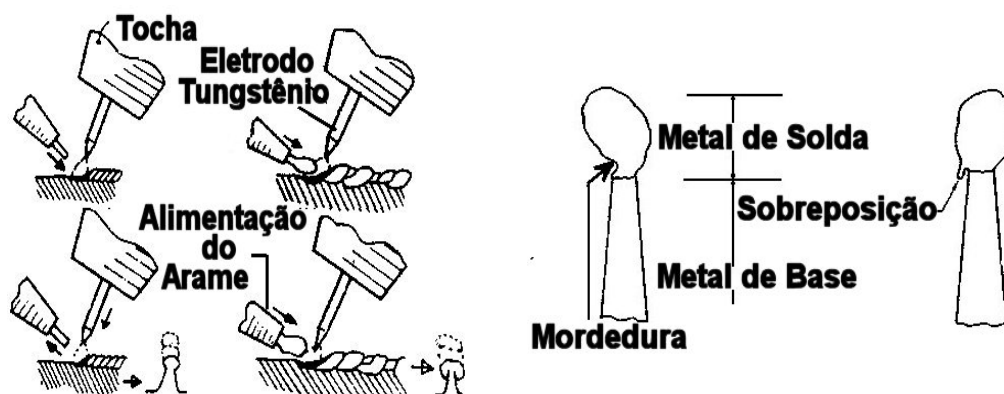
Soldagem TIG com arame pulsado e convencional (esquerda) e defeitos de soldagem em facas de SARD (direita).
